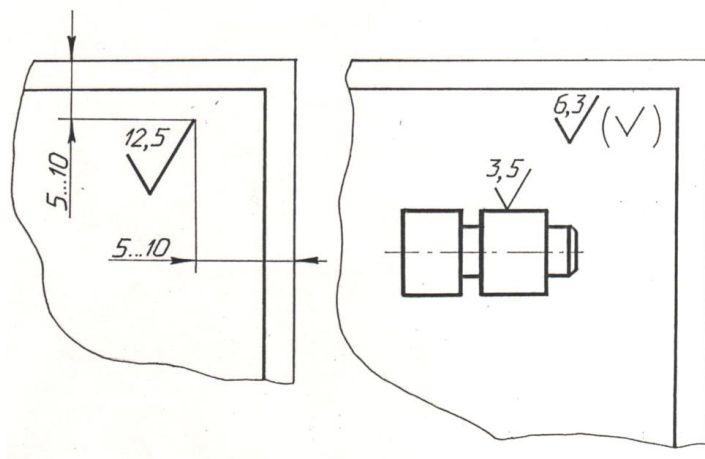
Обозначение шероховатости поверхностей деталей
